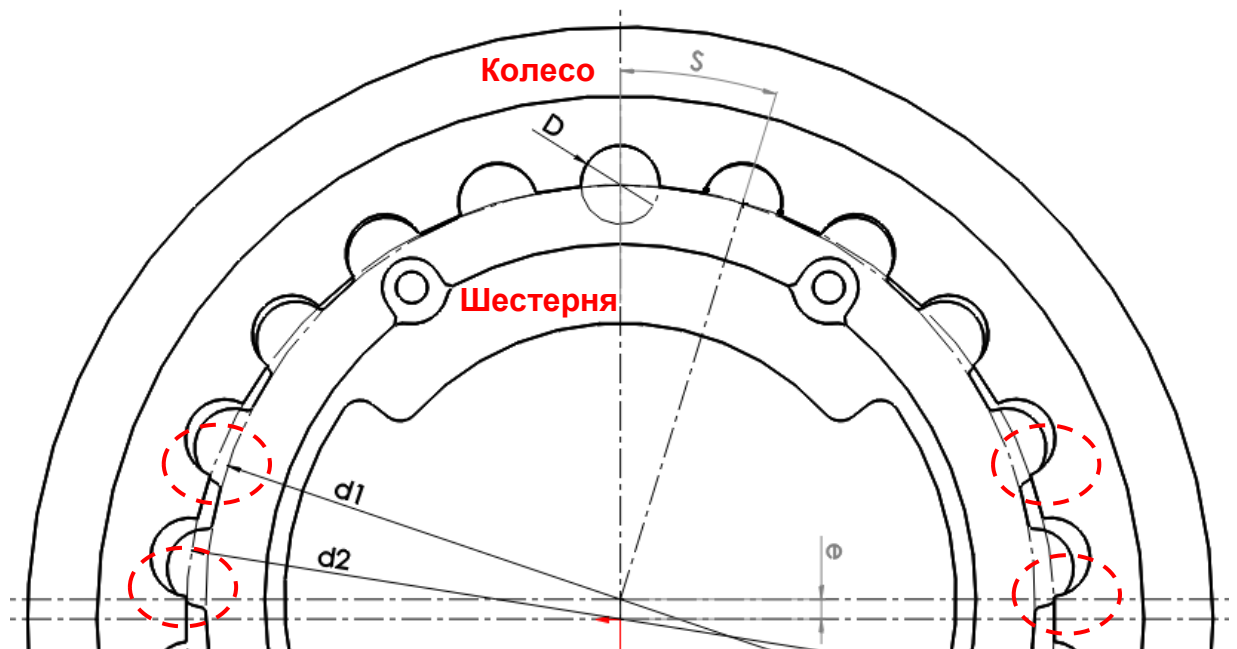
Модифицированный зуб шестерни и профиля зуба колеса.
